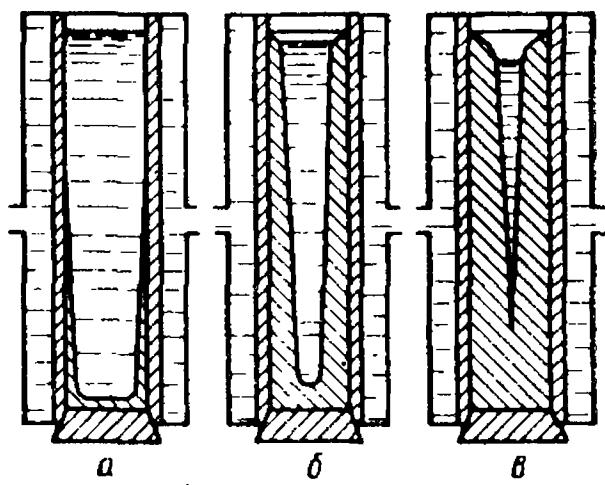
Схема перемещения границы твердой и жидкой фаз при формировании слитка в изложнице:
